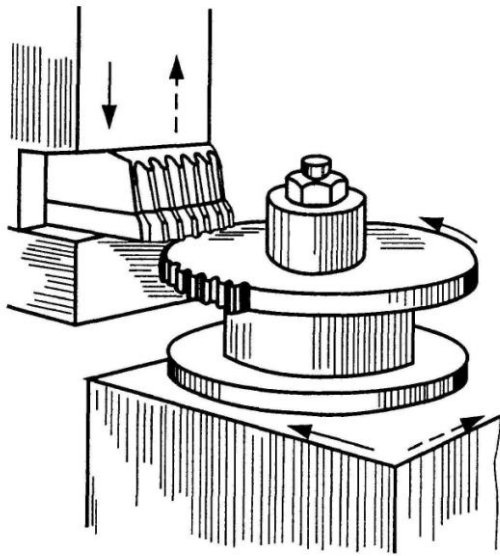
Нарізання зубчатих коліс інструментальною рейкою
